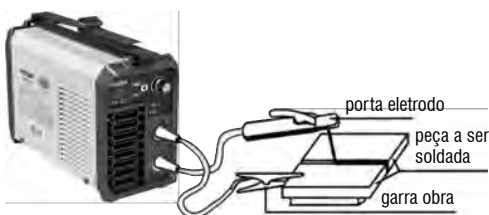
Montagem dos cabos de solda para soldagem de Eletrodo Revestido (MMA)
